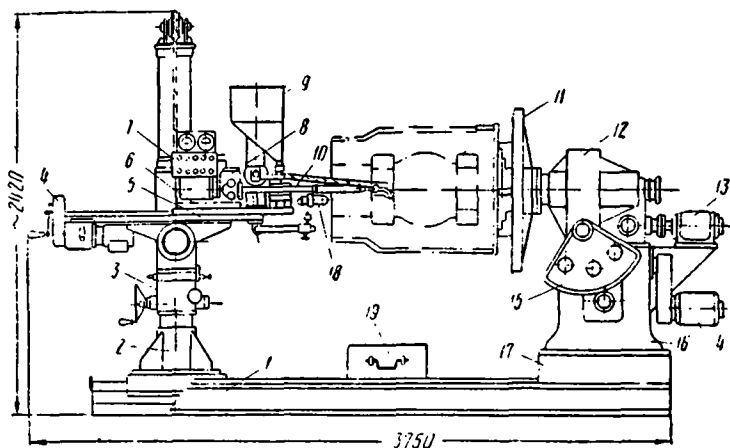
Установка для автоматической наплавки деталей электрических машин:
